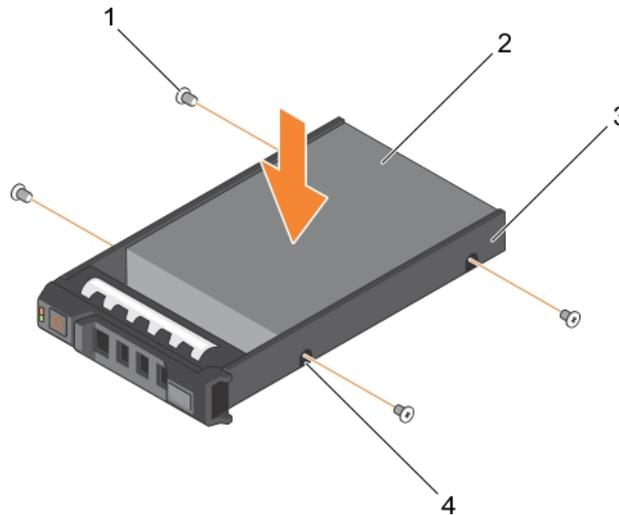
Installation d'un disque dur ou SSD de 2,5 pouces dans un support de disque dur ou SSD de 2,5 pouces
